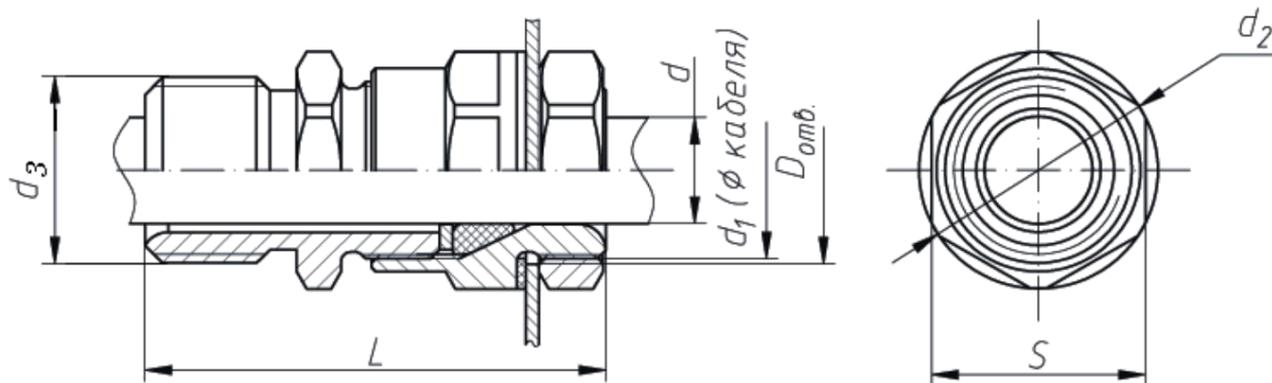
Кабельный ввод для прокладки кабеля в трубе (тип Т)
